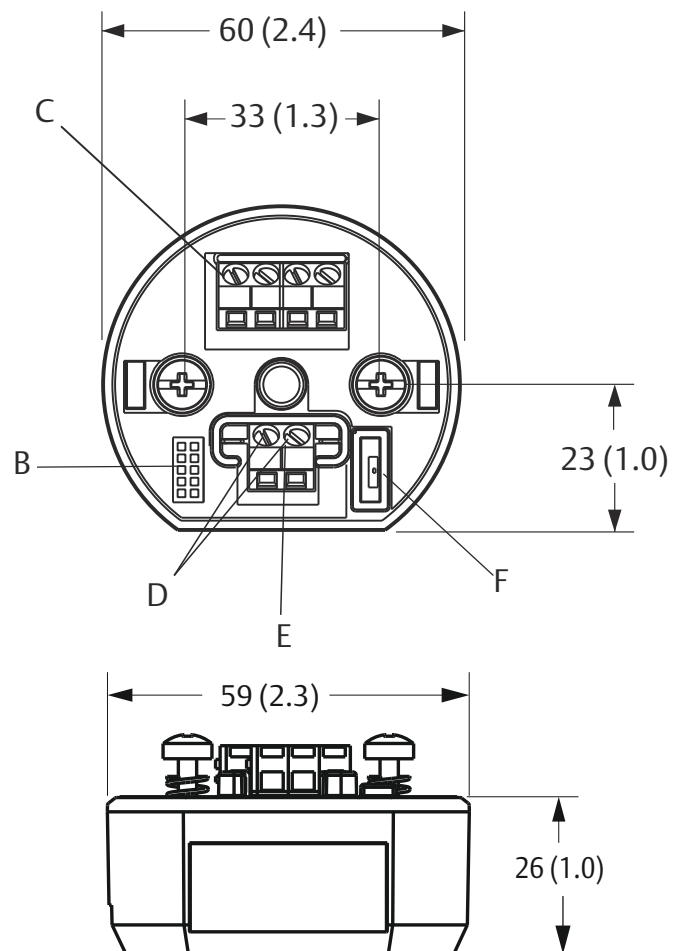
Rosemount 644H (montaggio su testa DIN A)
